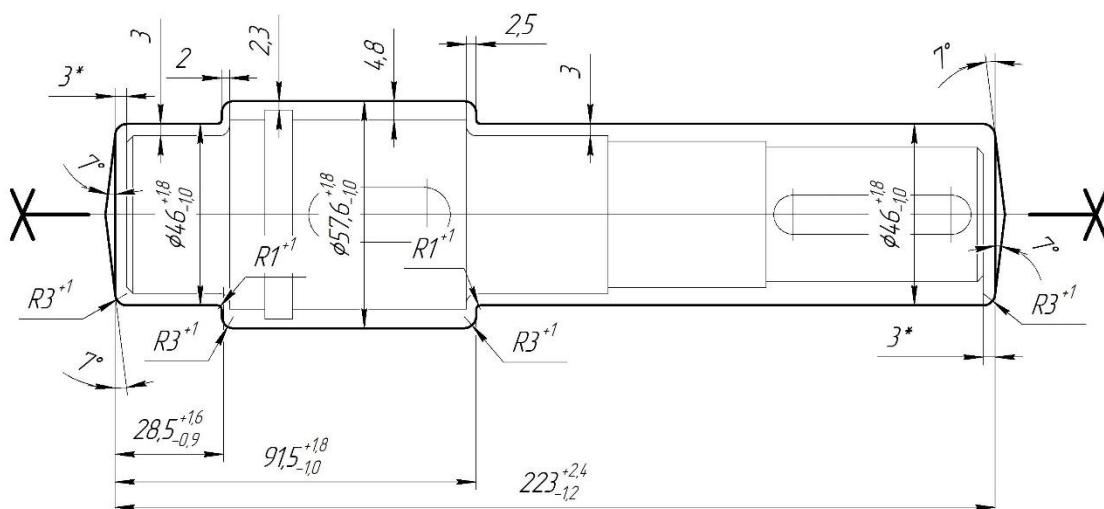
Ескіз кресленика заготовки деталі «Вал тихохідний»
